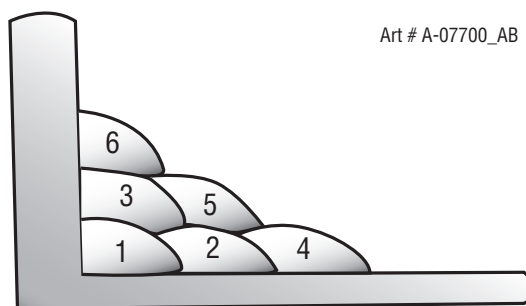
Plusieurs cordons dans la soudure du joint HV
